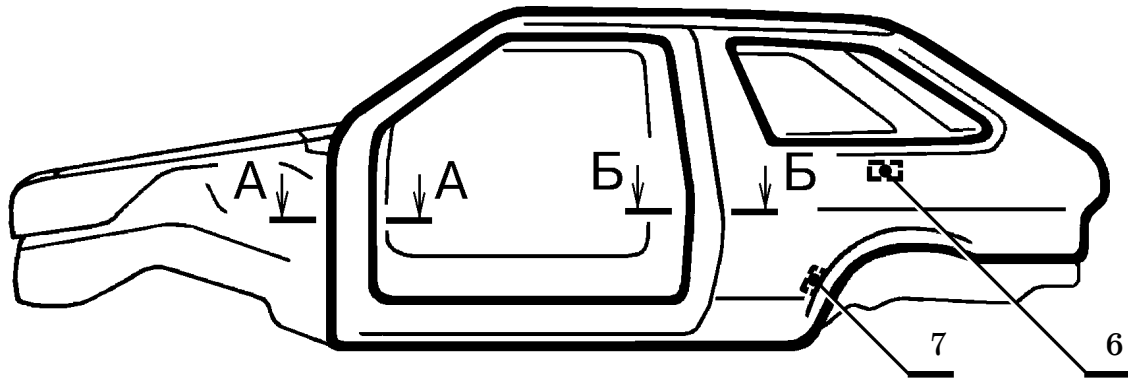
Детали боковины ВАЗ-2108 правой/левой: установка и приварка усилителей на панели боковины. Номера и наименования деталей, количество сварочных точек приведены в таблице 4.
